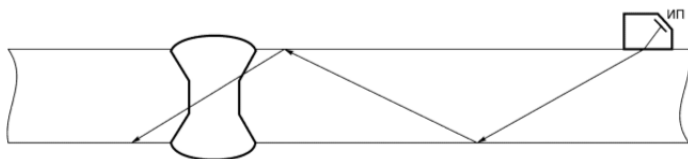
Схема прозвучивания стыкового сварного соединения двукратно отраженным лучом
